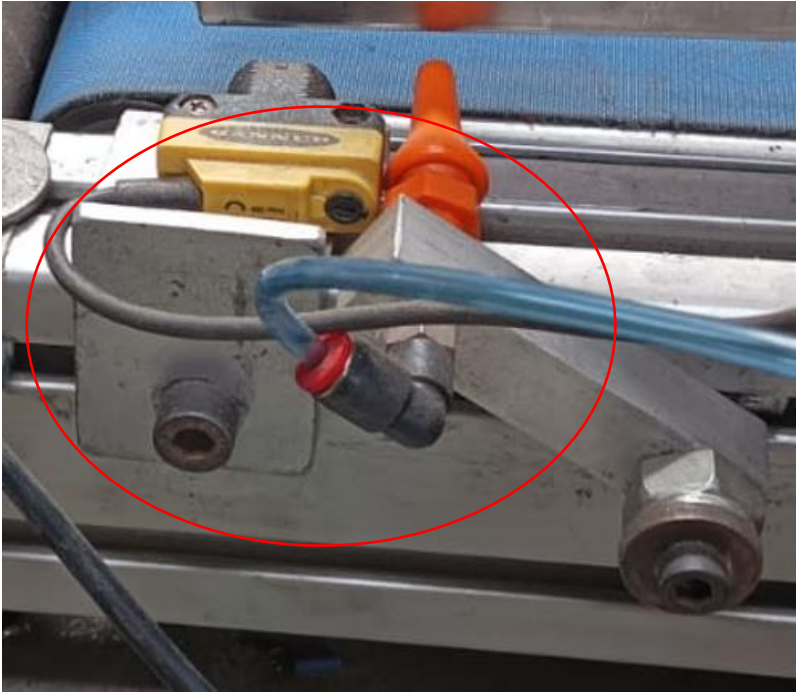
Montaje del acoplamiento para el sensor autorefectivo 1
